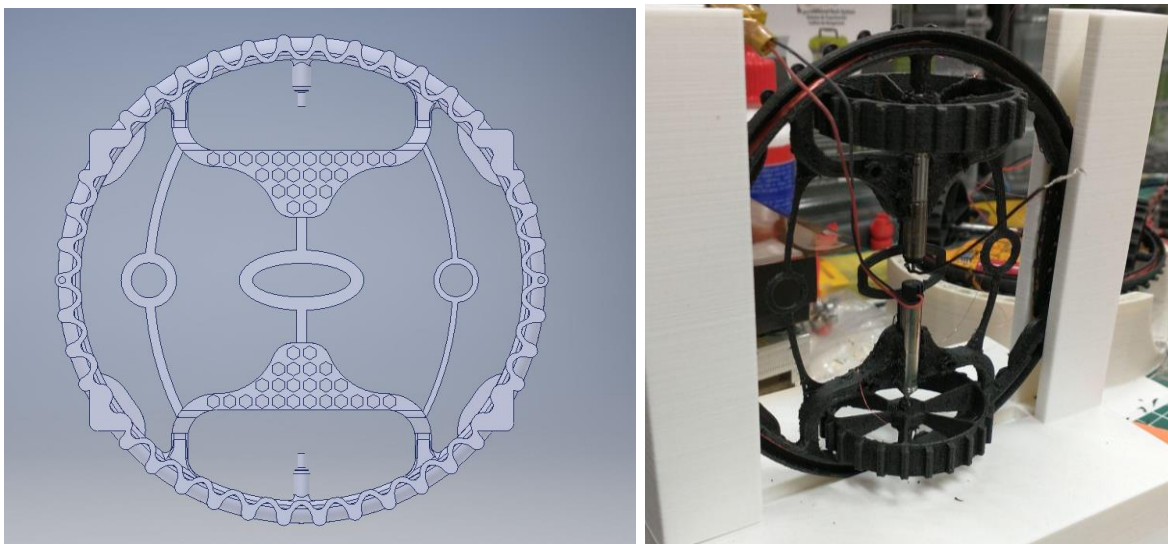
Diseño CAD y preparación para ensamble de la quinta versión del mini rover.
